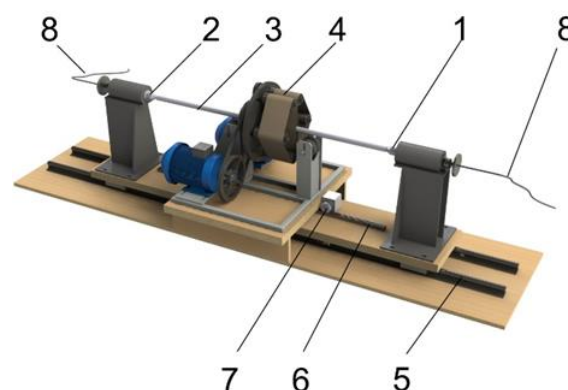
Схема установки для измерения сил резания: 1, 2 – передний и задний тензометрические центра соответственно; 3 – заготовка; 4 – установка для ротационного ленточного шлифования; 5 – направляющие станины; 6 – зубчатая рейка; 7 – шаговый электродвигатель; 8 – провода, ведущие к прибору для измерения сил резания
